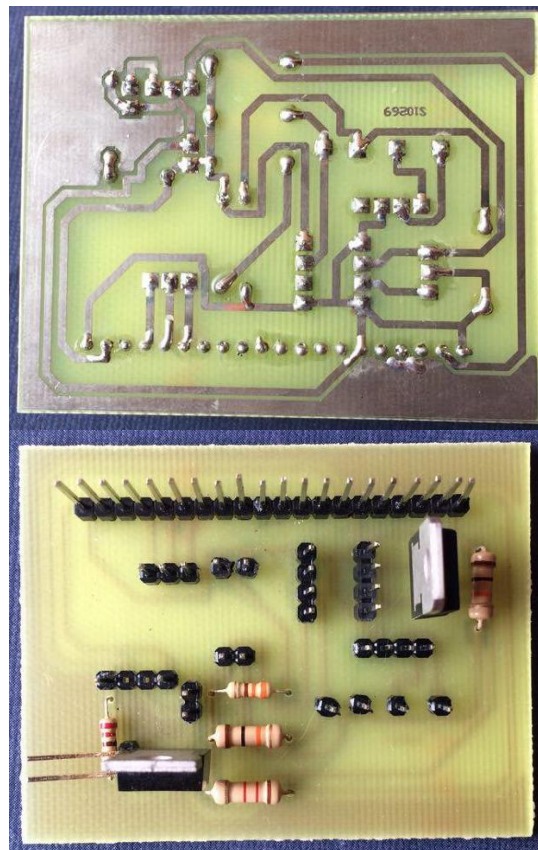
Vista posterior y frontal de la soldadura de los componentes.
